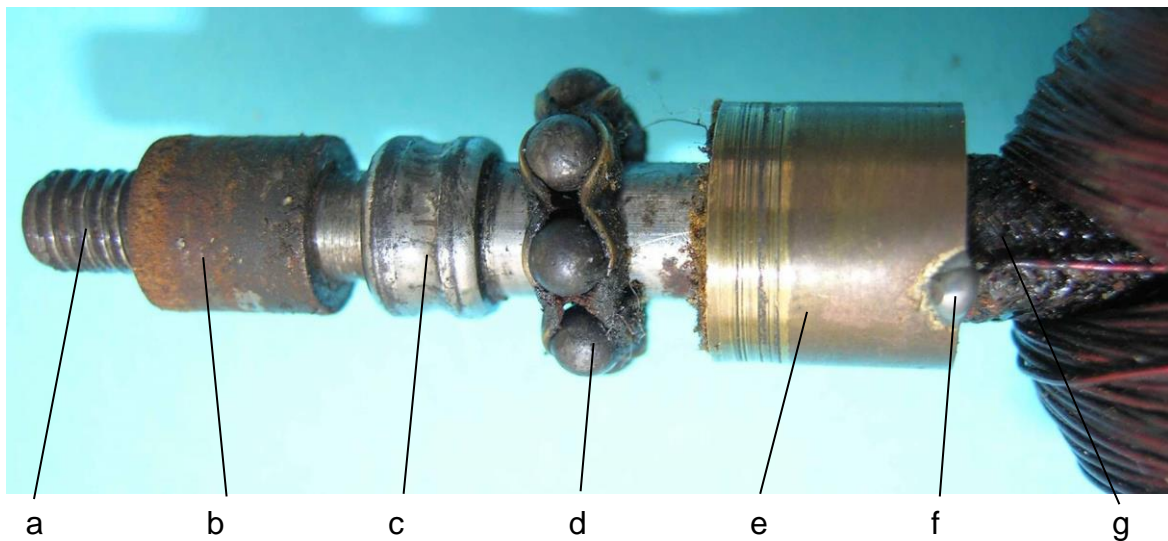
Obere Konstruktionselemente des Läufers: a) Welle mit Gewinde, b) Abstandshülse, c) Innerer Kugellagerring, d) Kugellagerkorb mit Kugeln, e) Schleifring, f) Lötkontakt, g) Wellenisolierung
